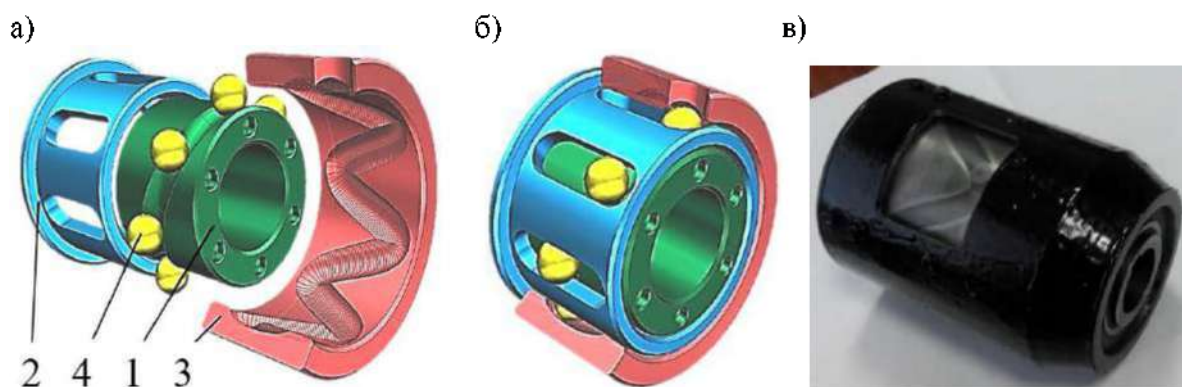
ППТК цилиндрического типа: а – основные элементы; б – передача в сборе; в – натурный образец.
